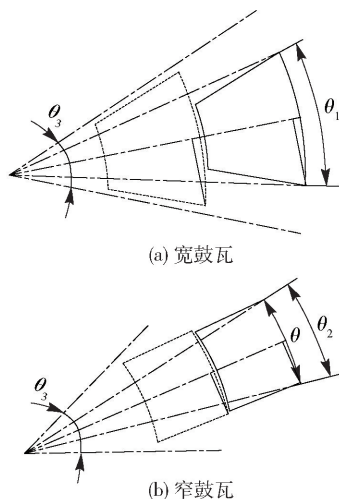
阶梯式内模宽、窄鼓瓦收缩干涉分析图
